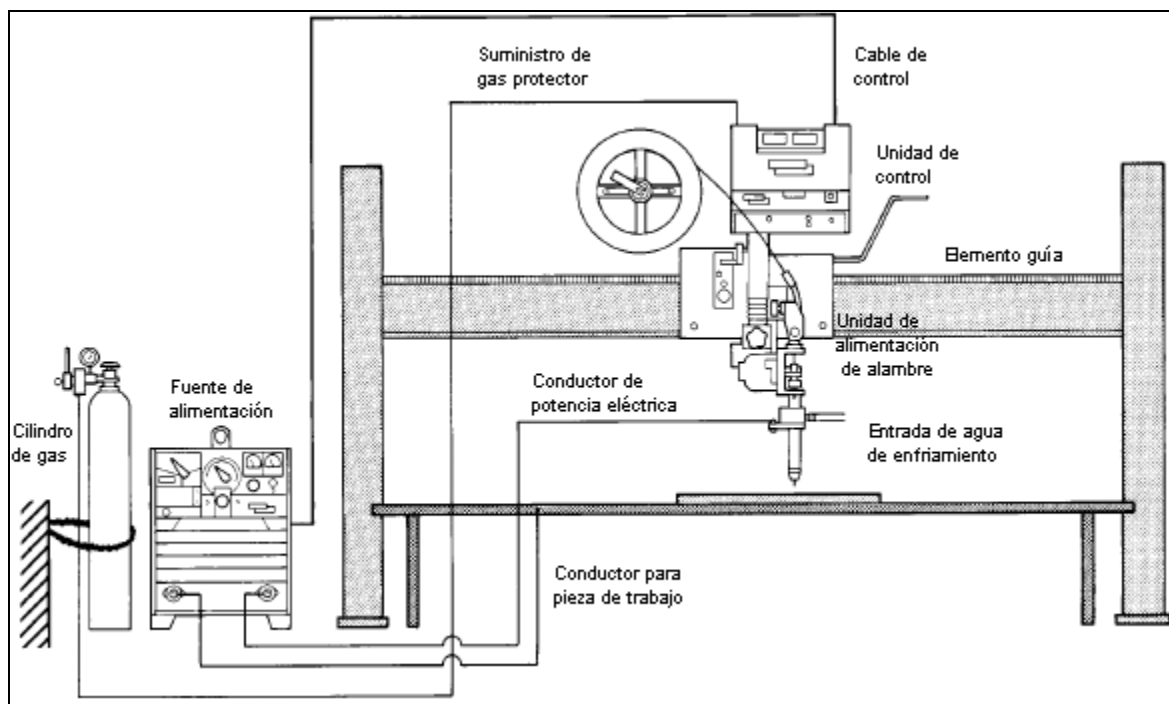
Proceso de soldadura GMAW automático^[11]
